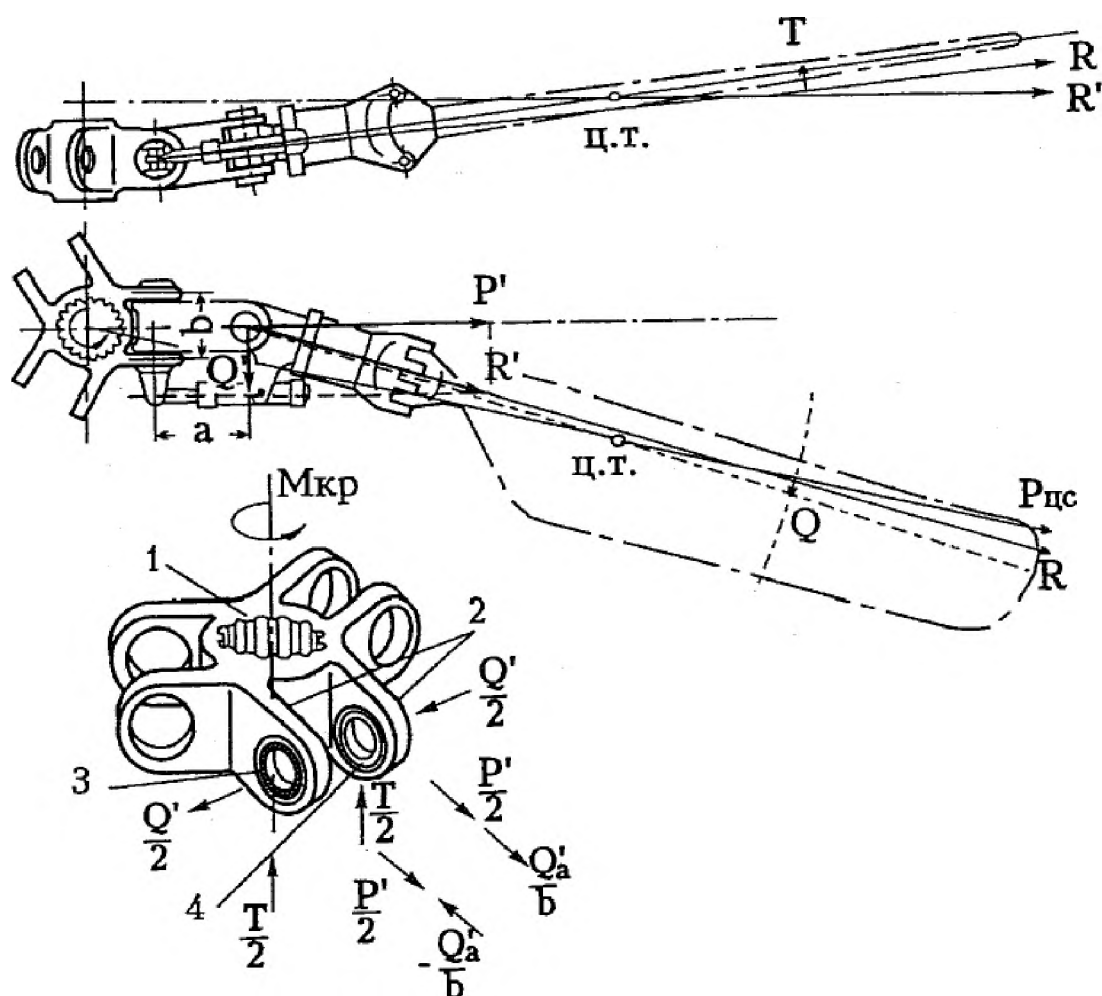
Схема нагружения ступицы шарнирной втулки:
